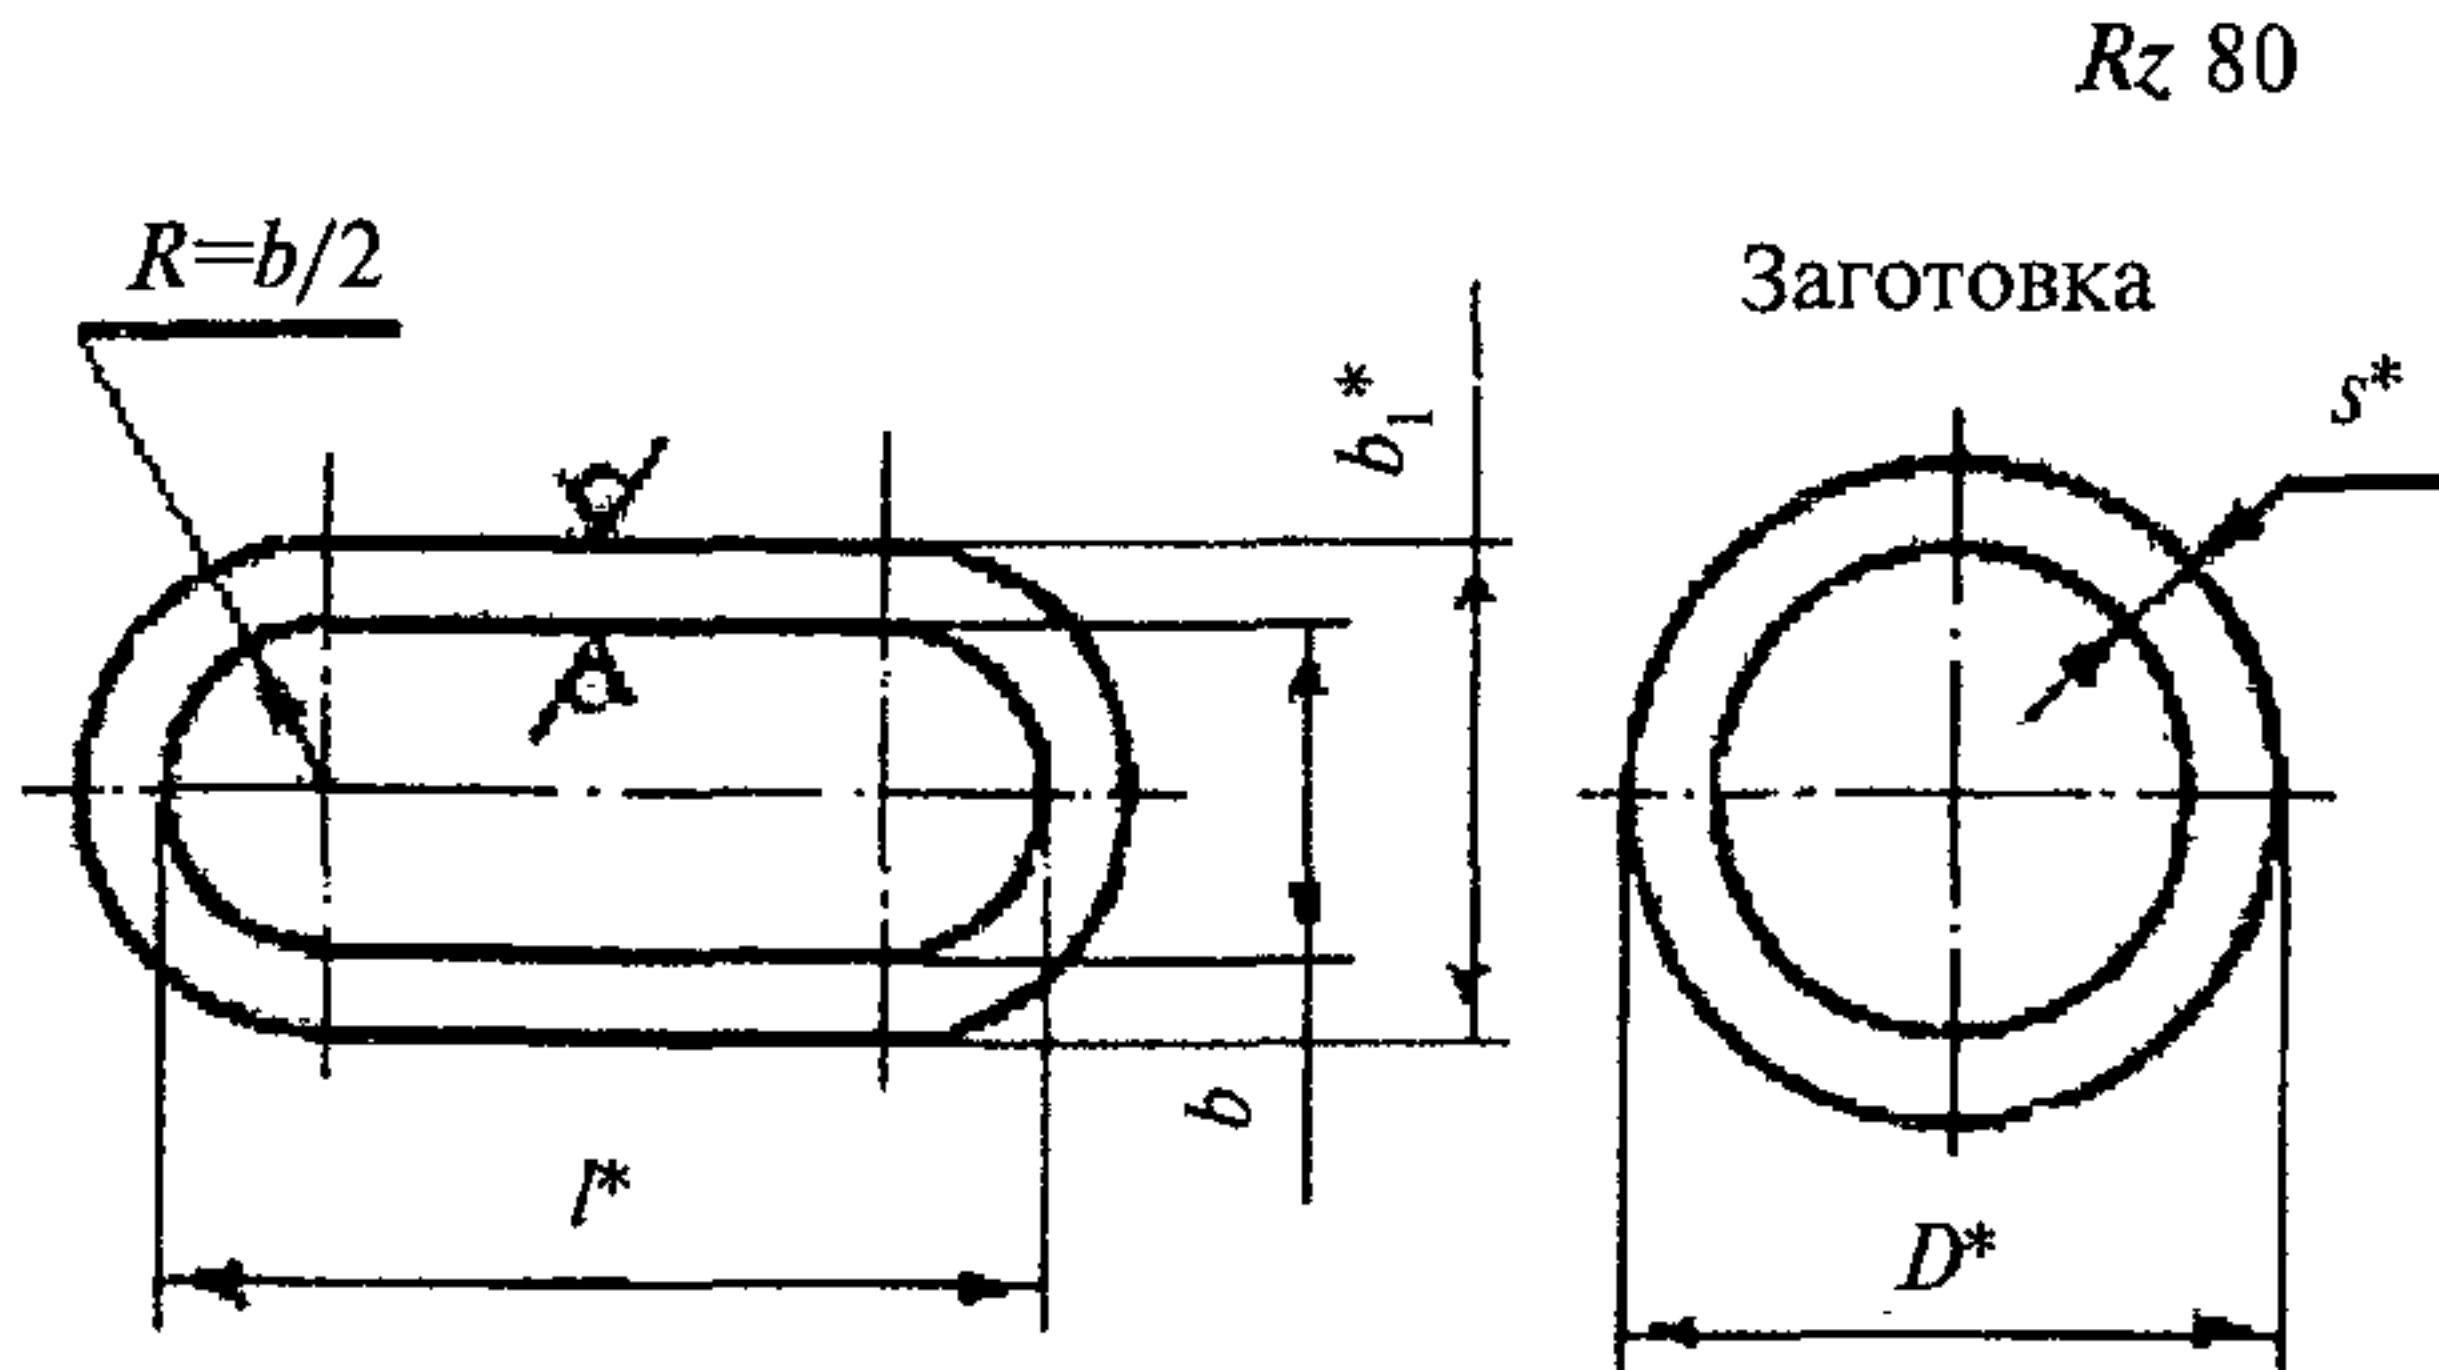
Заготовка стальной втулки и стальная втулка
